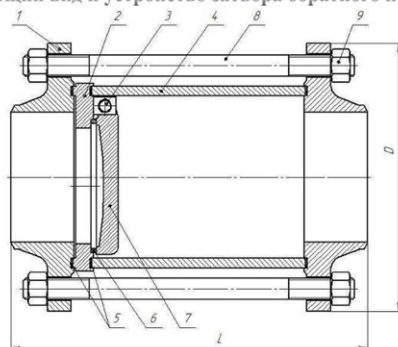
Общий вид и устройство затвора стяжного обратного поворотного*.
